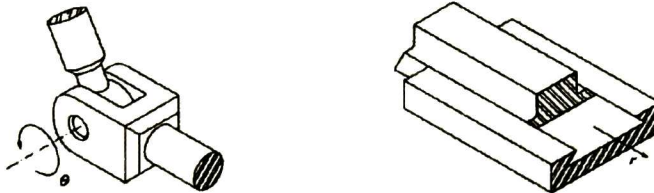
Uniones: Rotativa (izquierda) y Prismática (derecha).
